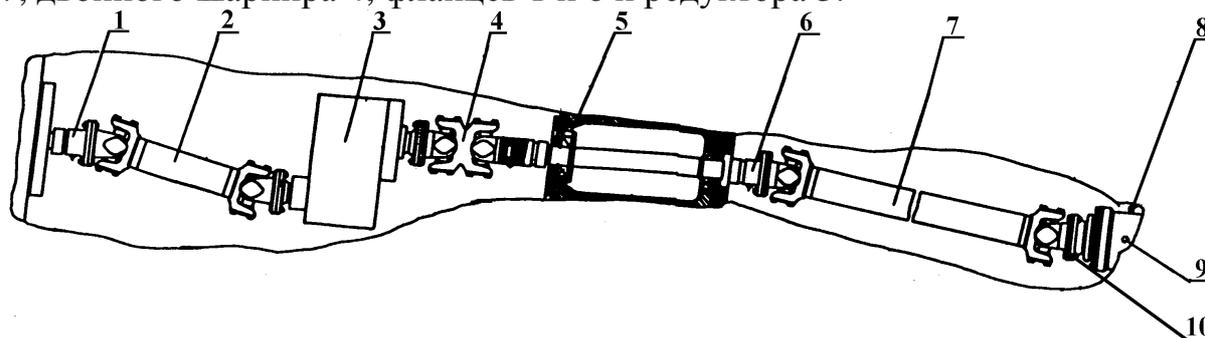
Привод заднего моста: 1, 6 – фланцы; 2, 7 – карданные валы; 3 – редуктор передней опоры; 4 – двойной шарнир; 5 – шарнир; 8 – сапун; 9 – контрольная пробка; 10 – фланец ведущей вал-шестерни
